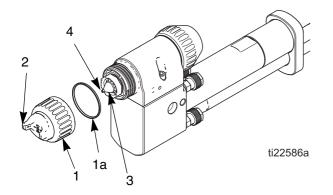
Limpieza del cabezal de aire y de la boquilla de producto
